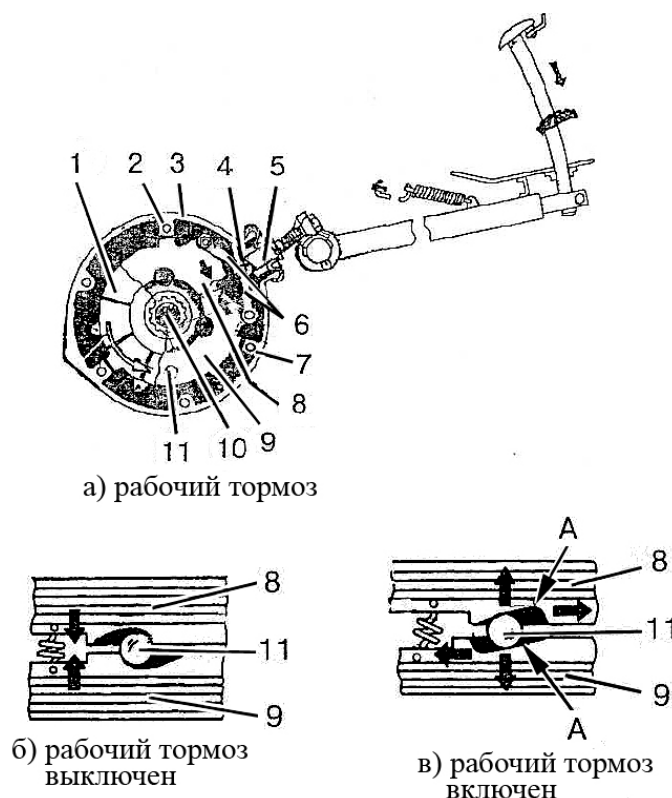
Устройство двухдисковых рабочих тормозов и управления рабочими тормозами
